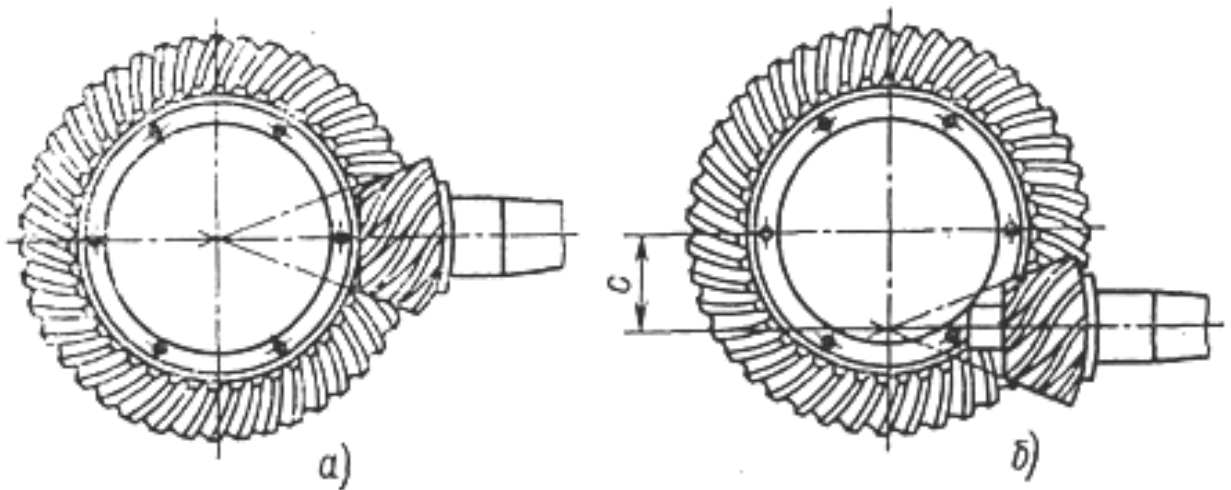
Схемы одинарной главной передачи с коническими шестернями
